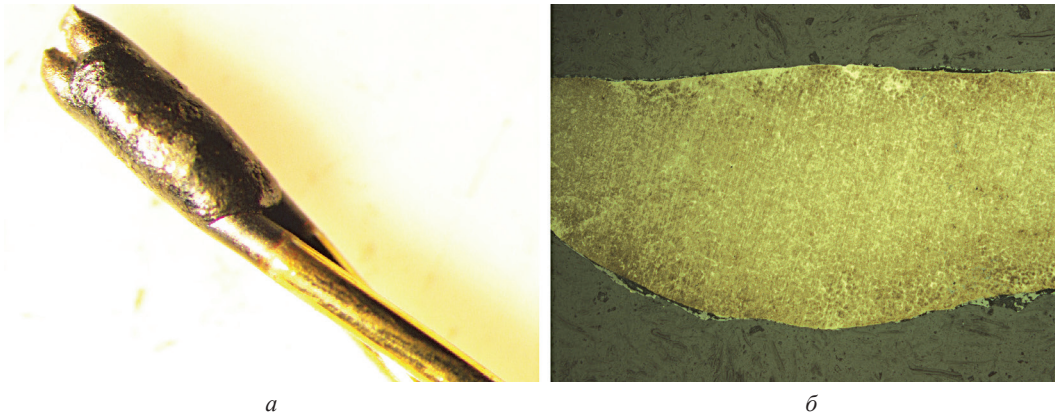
Сварка, выполненная с частичным отпуском на металлокорде конструкции 2×0,30 НТ: *а* – внешний вид разрушения после испытаний на разрыв. ×10; *б* – микроструктура сварного шва. ×200
